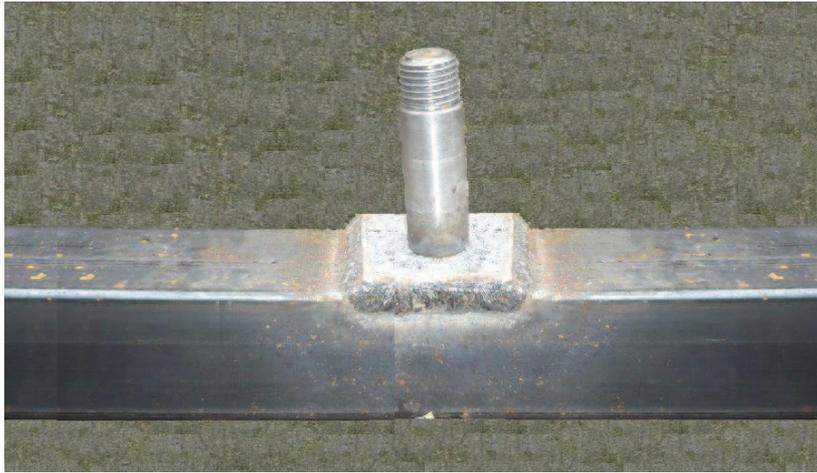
Punta de eje soldada ala parte superior del tubo estructural cuadrado
